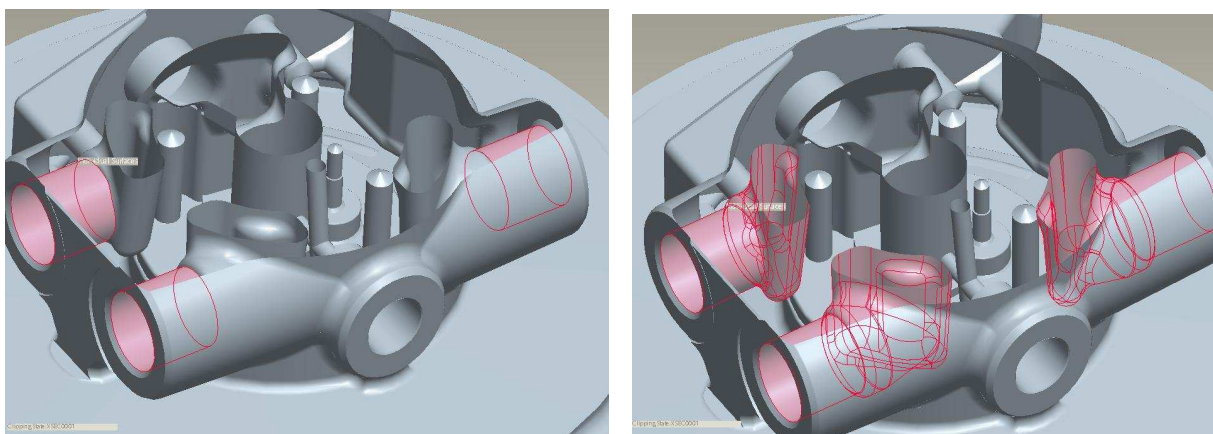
CAD model geometrie centrální skříně turbodmychadla
